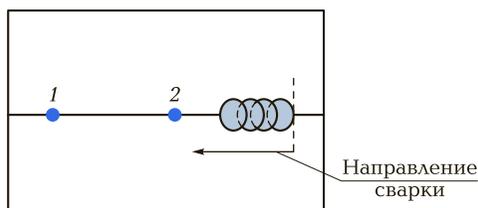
Схема сварки последовательным образованием сварочных ванночек:
